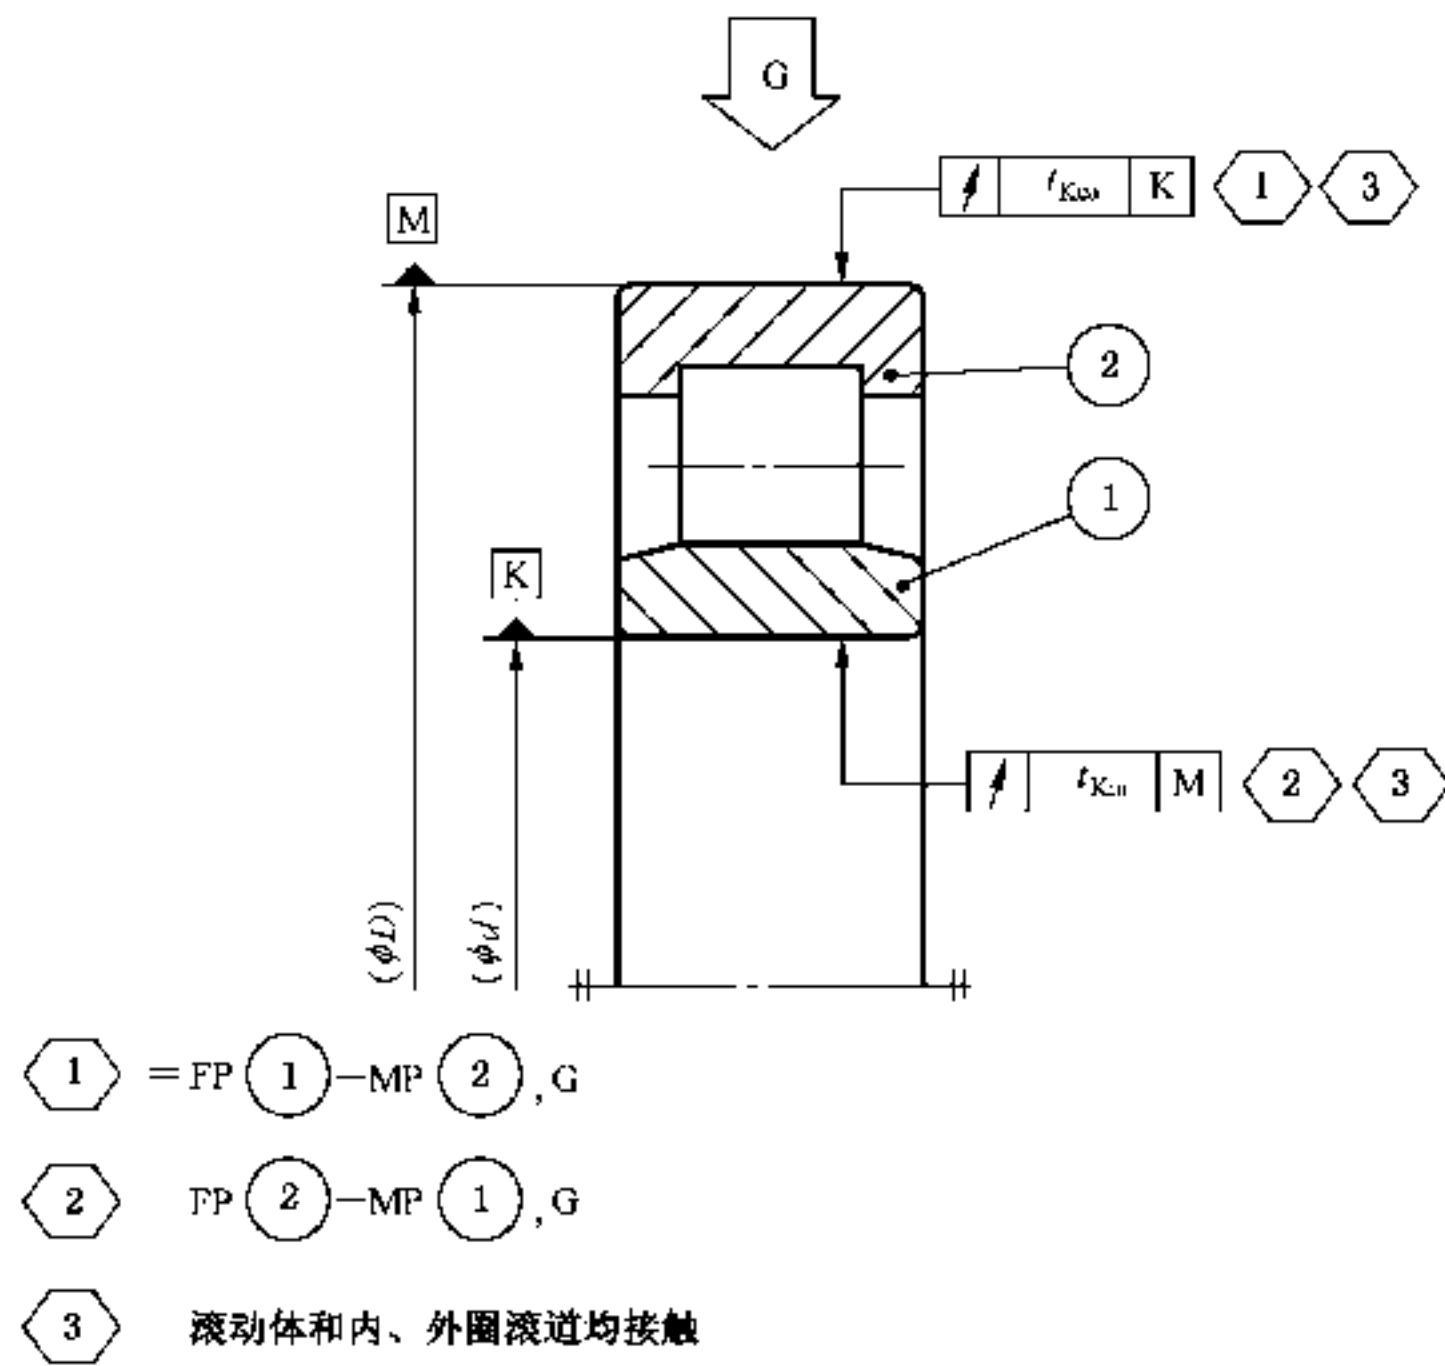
圆柱孔成套轴承的几何公差——圆柱滚子轴承、调心滚子轴承、长弧面滚子轴承和调心球轴承
